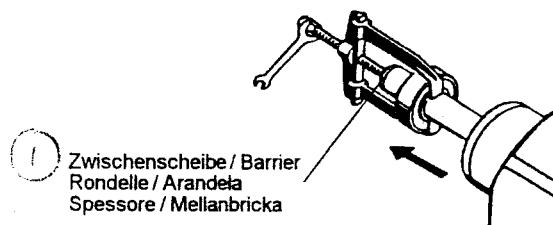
Lagerwechsel / Changing bearings / Remplacement des roulements
